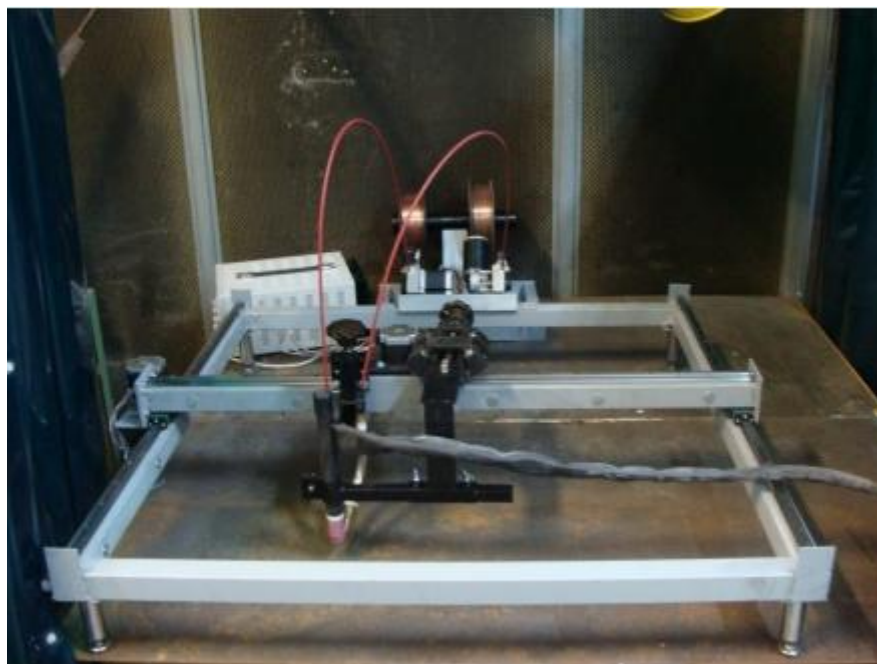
Установка для автоматической аргонодуговой наплавки
